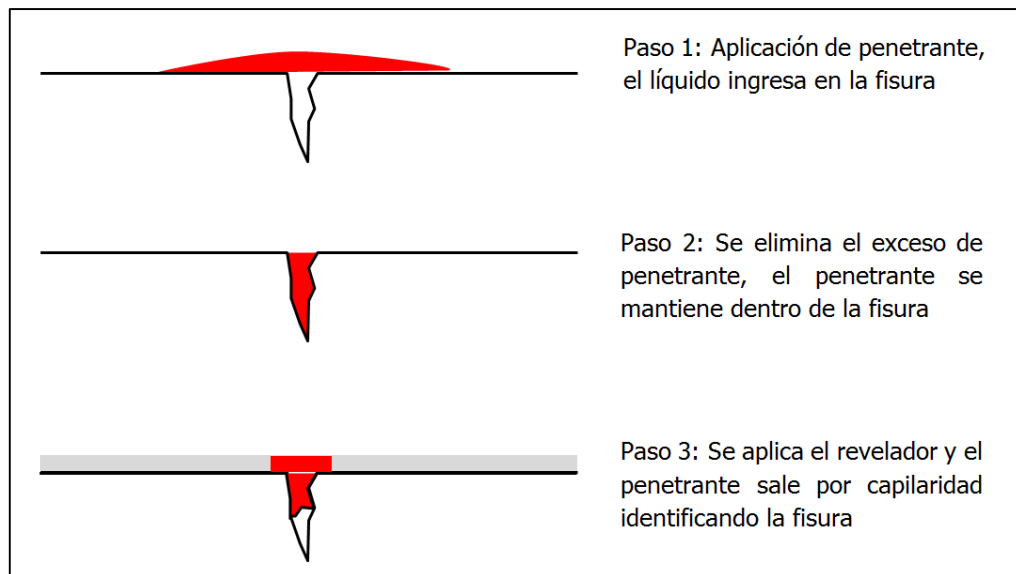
Procedimiento de pruebas con líquidos penetrantes en soldaduras
